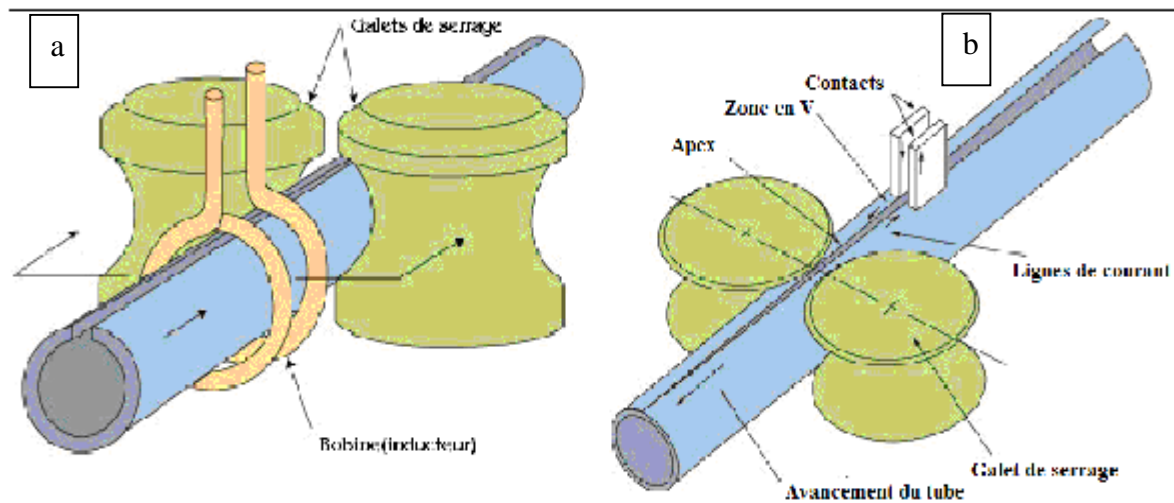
Chauffage des tubes: a) par induction, b) par contact [12]
